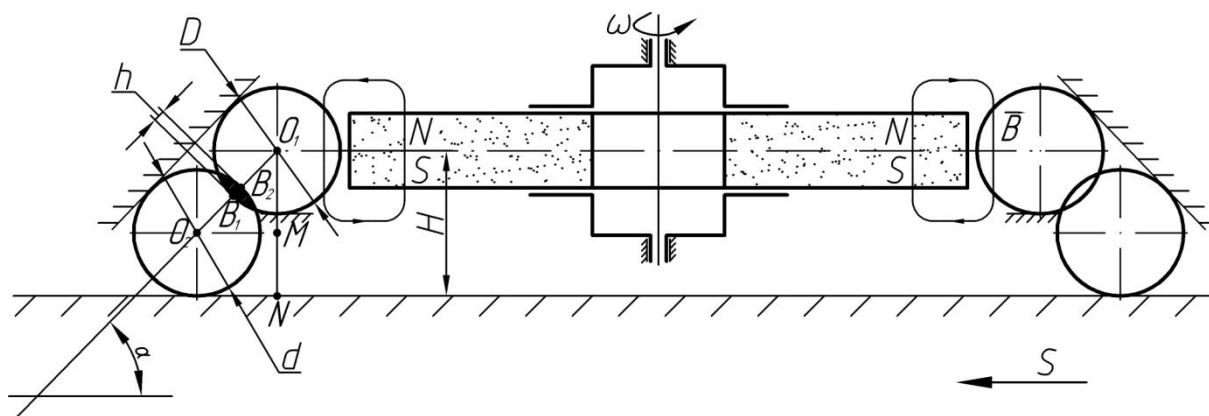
Схема магнитно-динамического накатывания плоских поверхностей деталей машин
